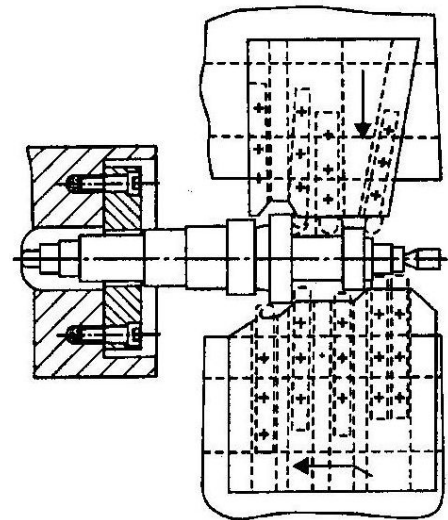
Наладка токарного багаторізцевого напівавтомата для обробки ступінчастого вала
